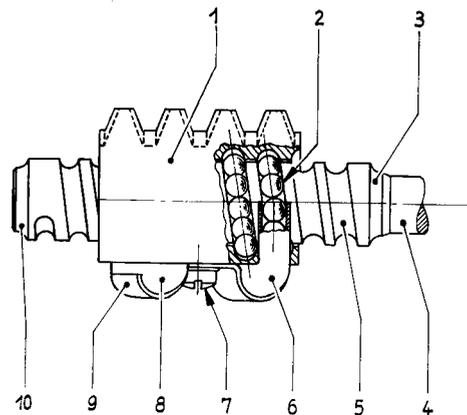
Anordnung der Lenkspindel mit Lenkmutter
